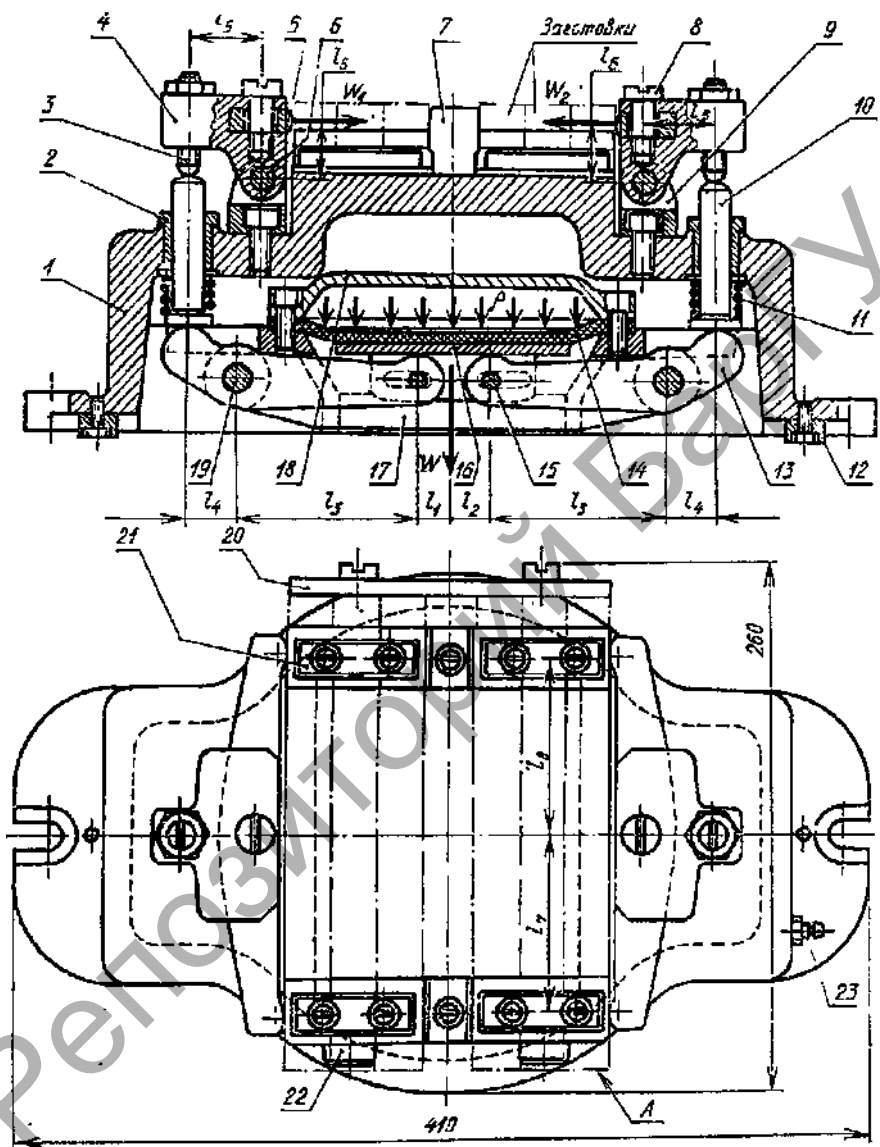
Фрезерное многоместное приспособление для обработки торцов заготовок типа планок со схемой комбинированной передачи сил зажима
